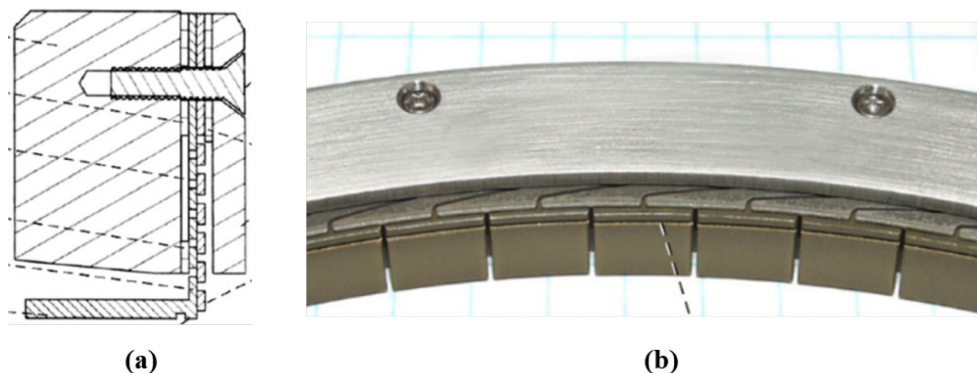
Vue en coupe de joints à doigts sans contact (a) et photo d'un prototype (b) [13]
